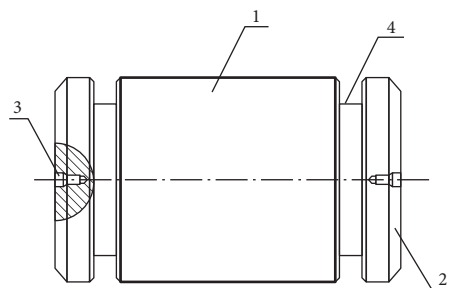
Конструктивное решение болта-шарнира: 1 — ось (шпилька); 2 — крышка; 3 — крепежный болт; 4 — паз для замка (шайба)
